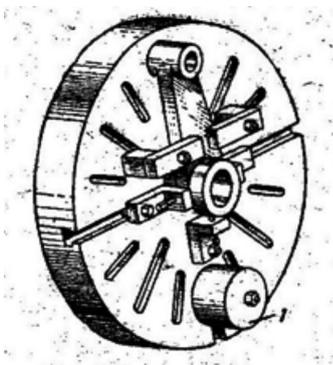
Патрон специальной конструкции с креплением обрабатываемой детали на планшайбе
